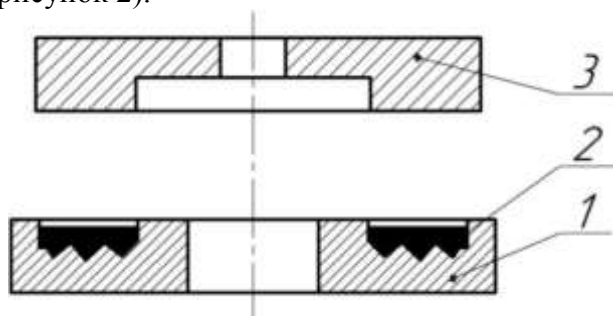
Схема прессования шихты в кольцевом пазу заготовки:
